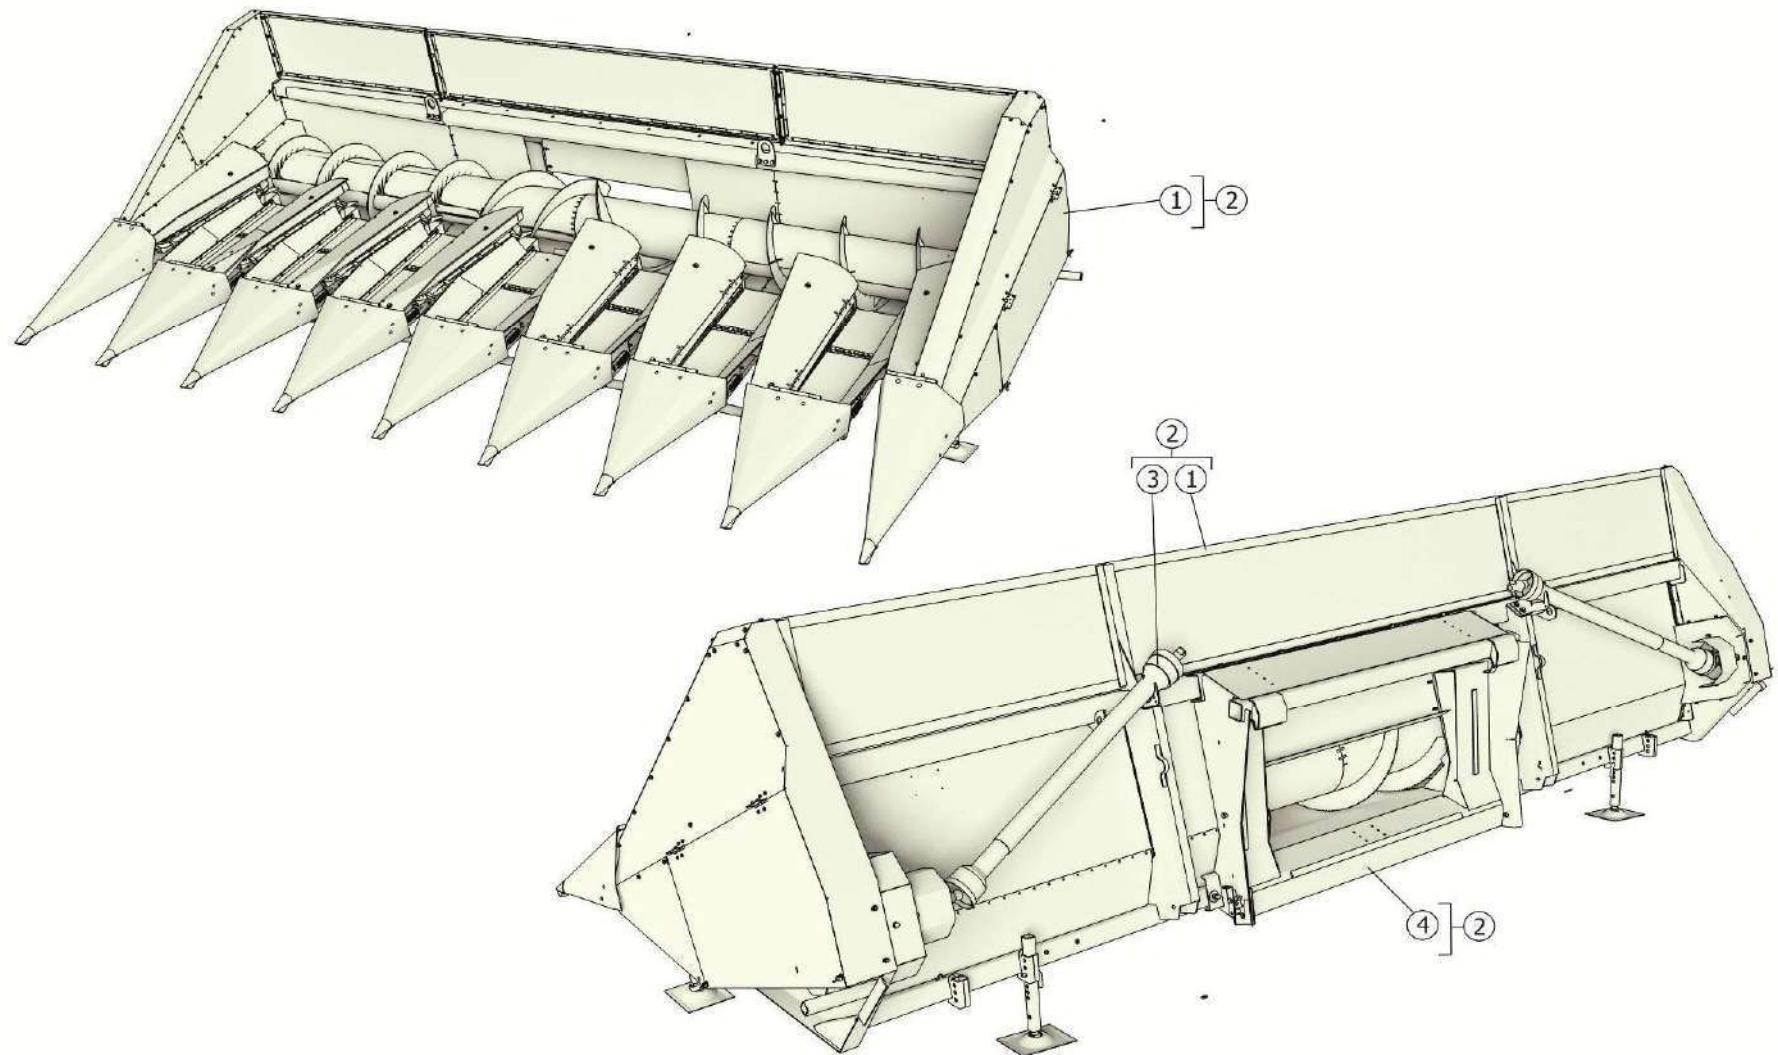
Приспособление для уборки подсолнечника ПСП-810.10.00.000-05
